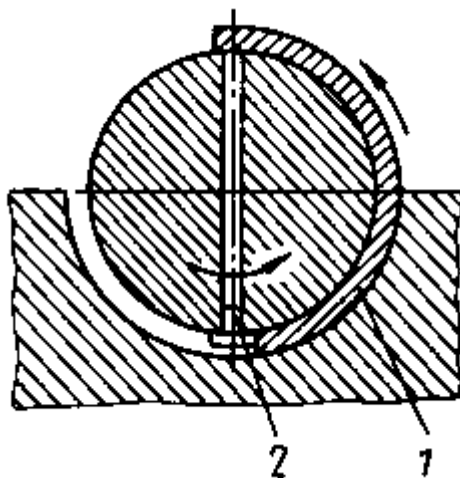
Выкатывание нижнего вкладыша коренного подшипника: 1 – вкладыш, 2 - штифт
